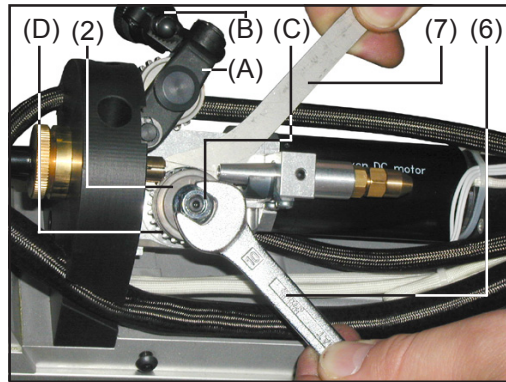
Förderrolle mit „Triebrod Motor“ montieren
